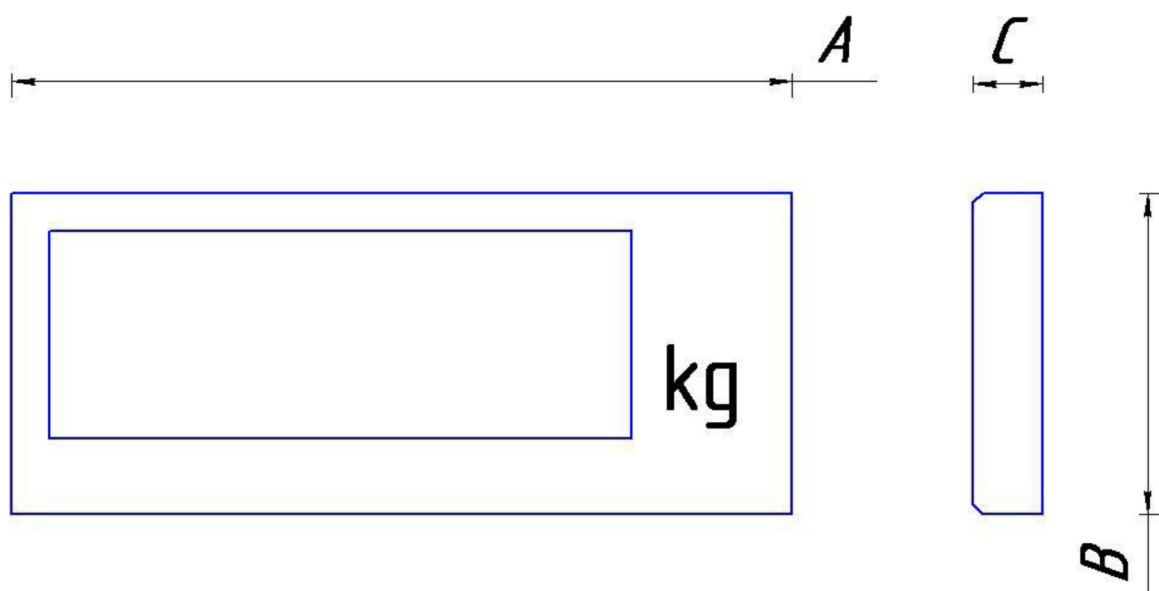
Общий вид и габаритные размеры дисплея
